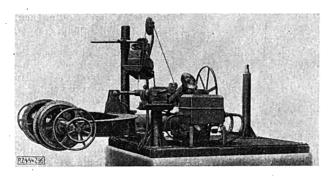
Selbständige Maschine für Auftragschweißung auf Räderlaufflächen
